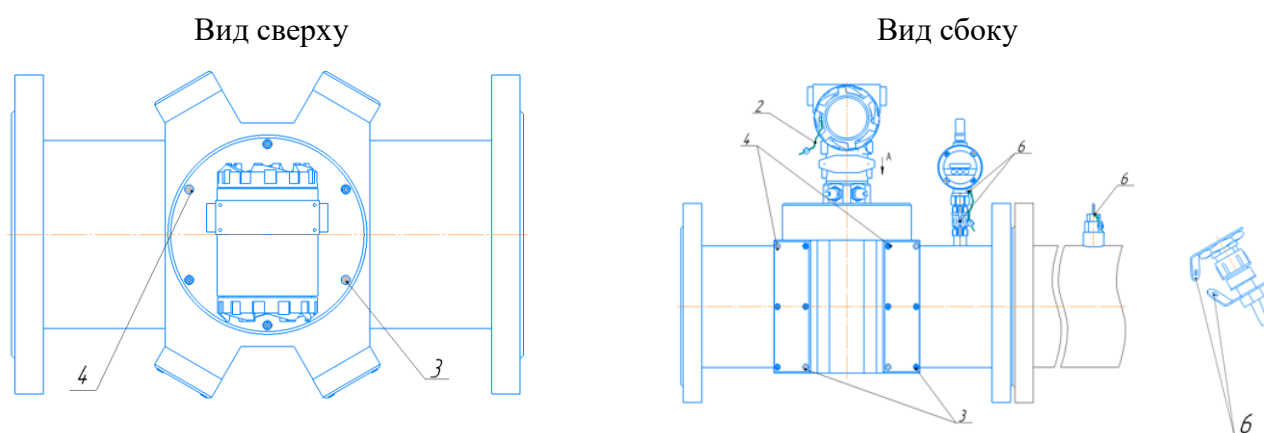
Корпус круглого сечения с отдельными защитными крышками
